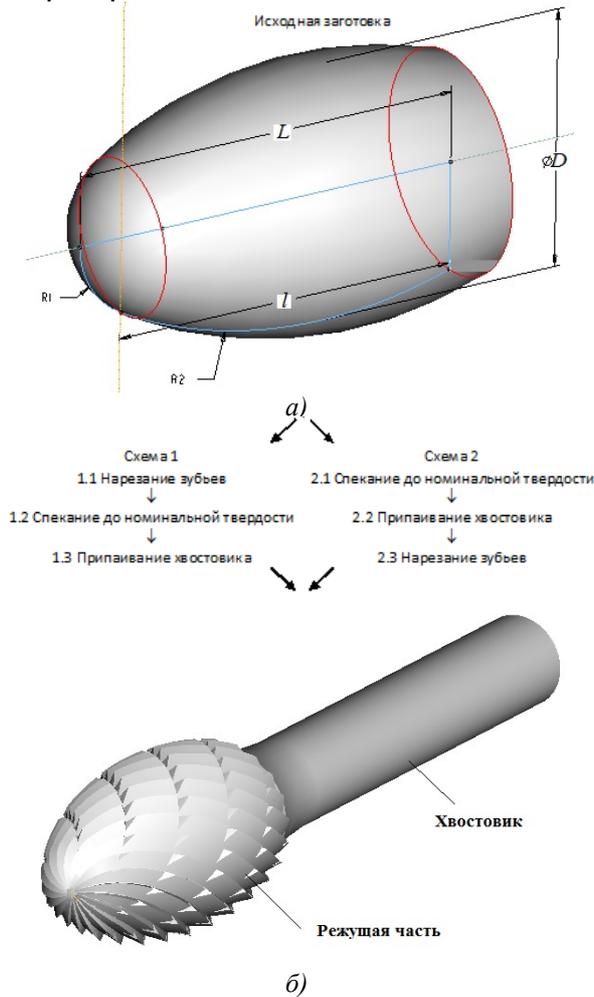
Схемы изготовления твердосплавных инструментов из заготовок, полученных прессованием
